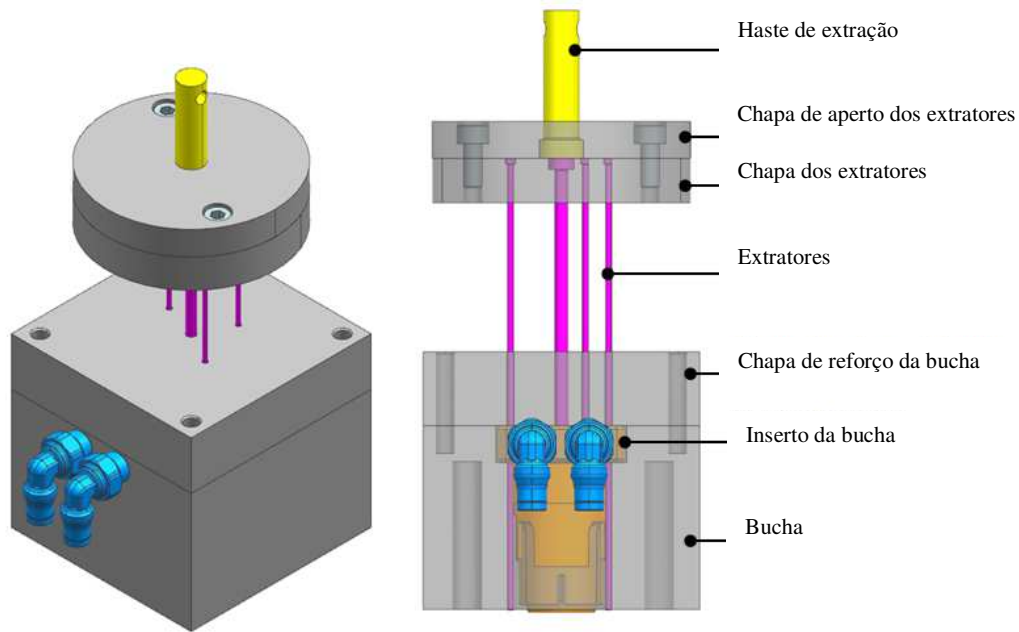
Lado da extração do molde de fabrico aditivo, *Sensor housing
